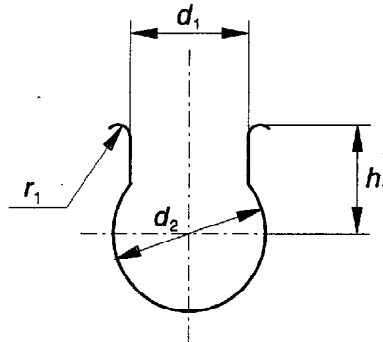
Dimensions des calibres NE PASSE PAS pour les tiges à rotule
